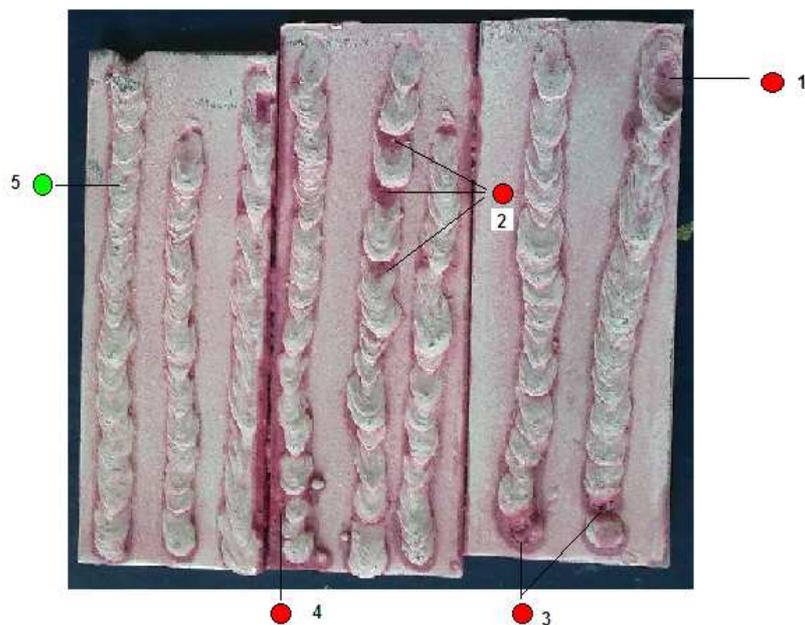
Fallas en la soldadura SMAW
